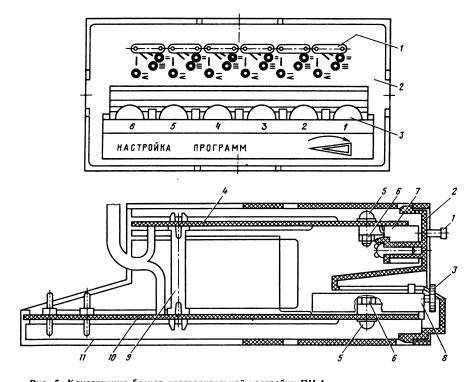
Конструкция блоков предварительной настройки ПН-1: I — перемычка переключателя диапазонов; 2 — лицевая панель; 3 — ручка регулятора настройки; 4 — плата 3У; 5 — винт; 6 — гайка; 7 — корпус переключателей диапазонов; 8 — переменный резистор регулятора настройки; 9 — распорка; 10 — плата 3K; 11 — корпус блока
